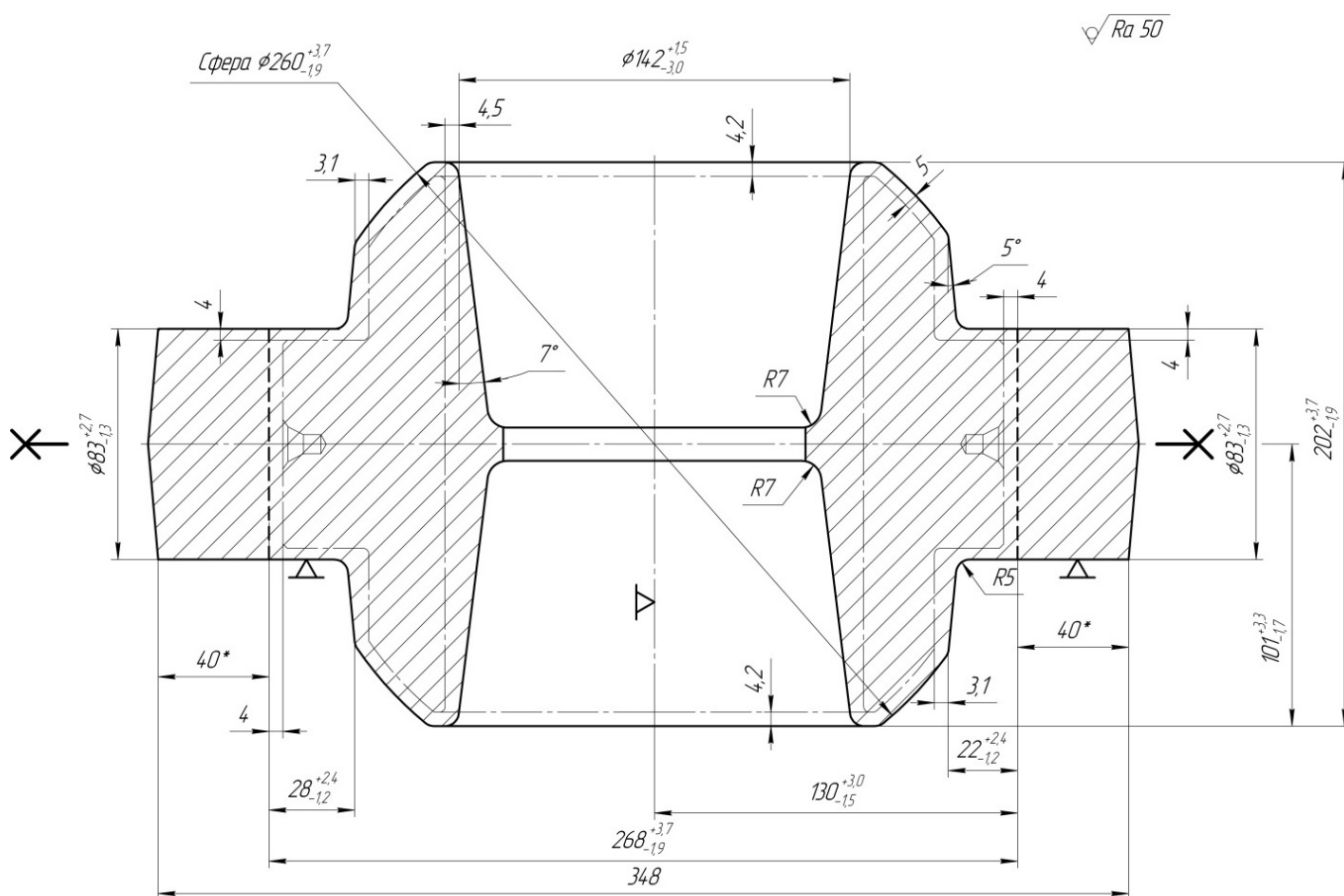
Ескіз заготовки виготовленої на КГШП
